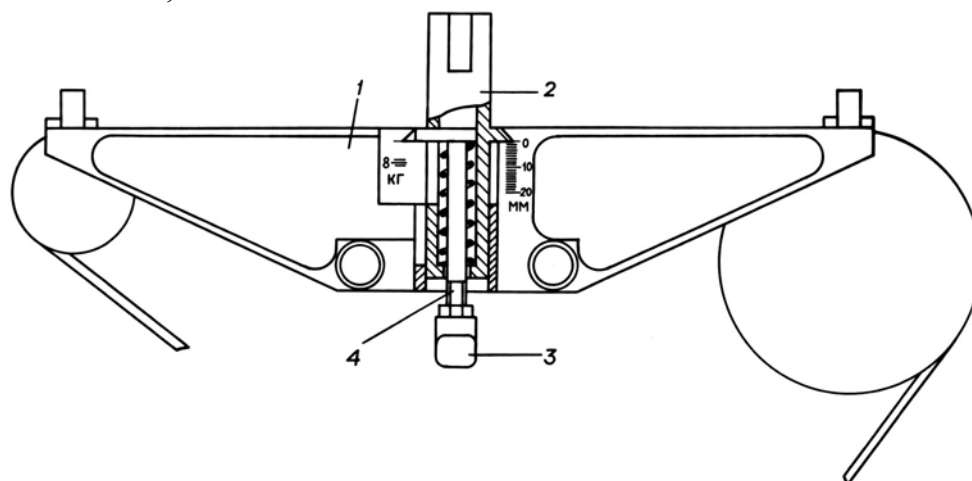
Проверка натяжения ремня привода агрегатов измерительным калибром:
